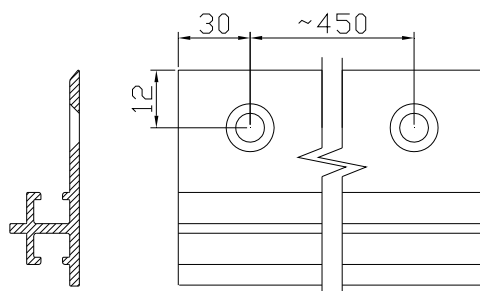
Схема сверления угловой алюминиевой стойки.
